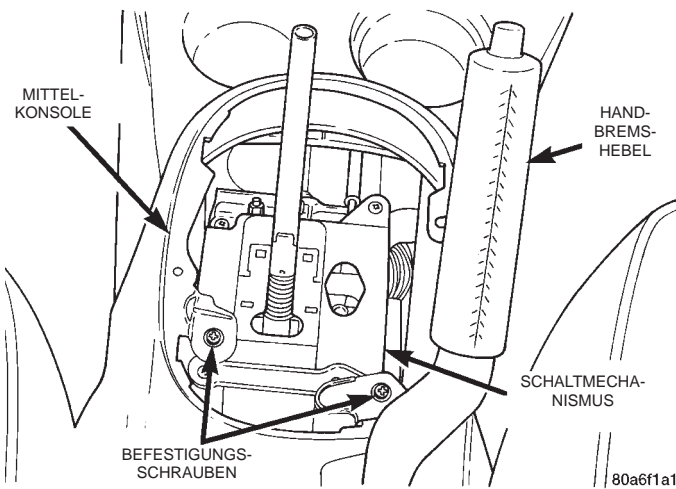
Vordere Befestigungsschraube der Mittelkonsole
